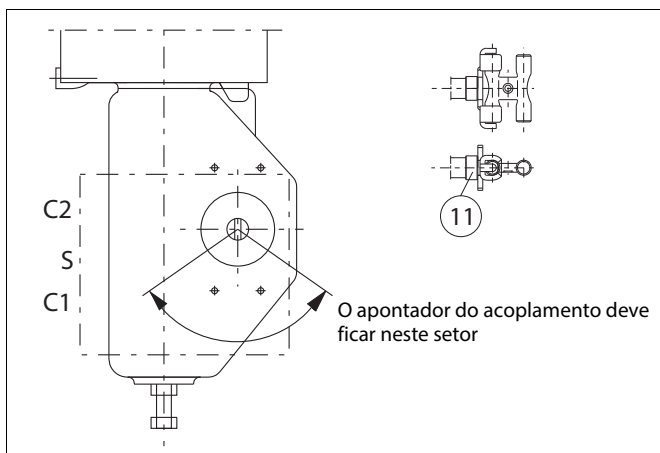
Montagem em atuador Neles com face de montagem VDI/VDE
